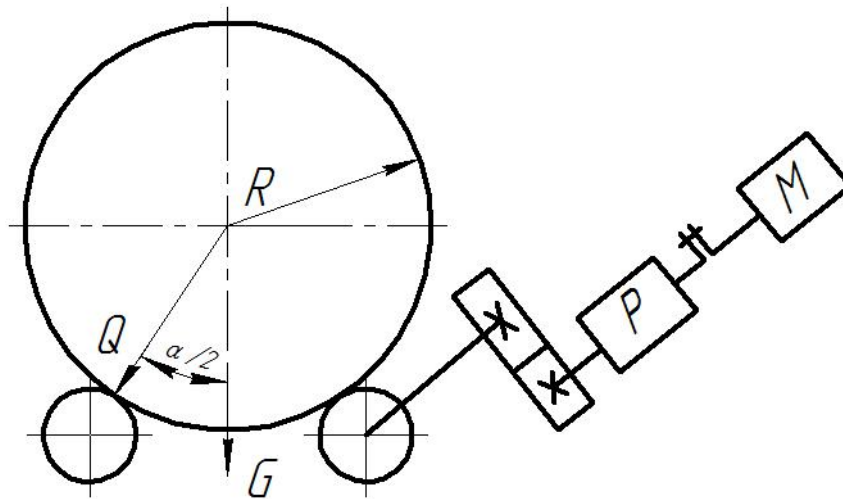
Розрахункова схема опор роликового стенда
